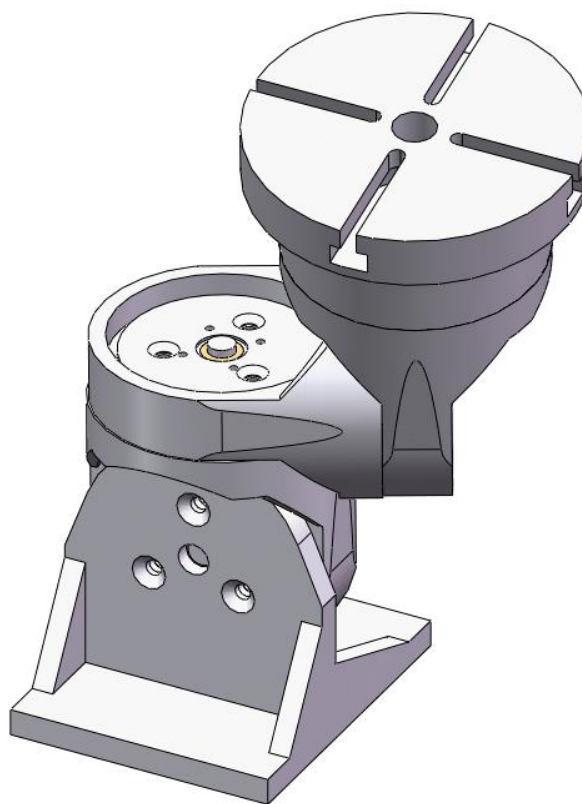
Конструктивный вид предложенного мехатронного устройства.
